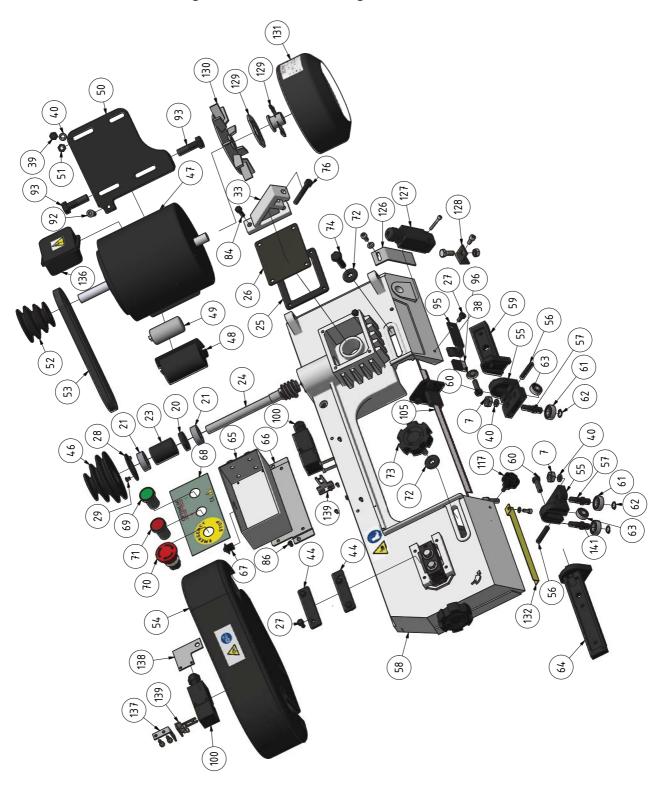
Ersatzteilzeichnung 1 von 4 - Parts drawing 1 of 4
